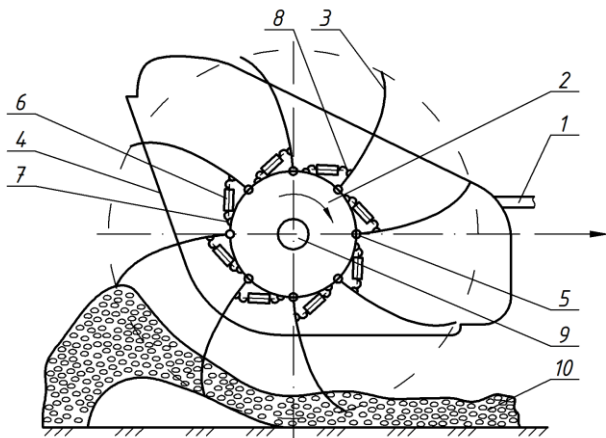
Робочий орган для ворущіння стебел льону: 1 – рама; 2 – диски; 3 – пальці; 4 – направляючі поверхні; 5 – шарнірні з'єднання; 6 – римська гайка; 7 – з'єднання дисків з гвинтами; 8 – шарнірні з'єднання пальців із гвинтами римської гайки; 9 – вал дисків; 10 – стебла льону
